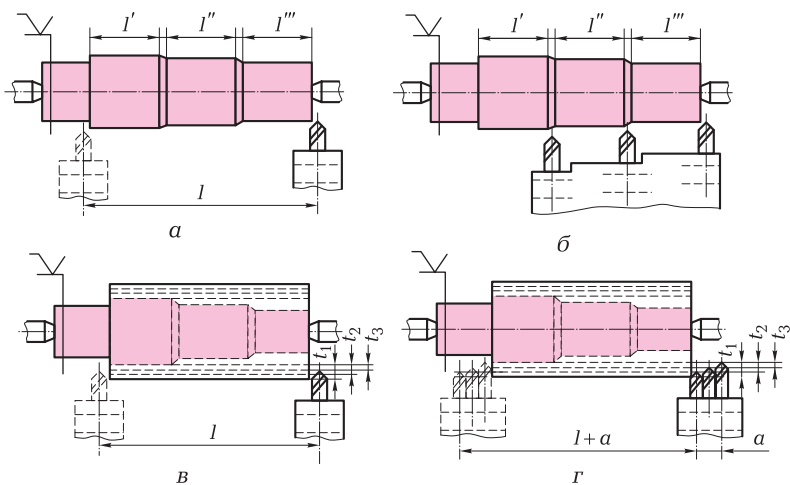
Схемы обработки наружной поверхности ступенчатого вала: а — на универсальном токарном станке; б — на многорезцовом токарном станке; в — за несколько рабочих ходов; г — с применением нескольких резцов
